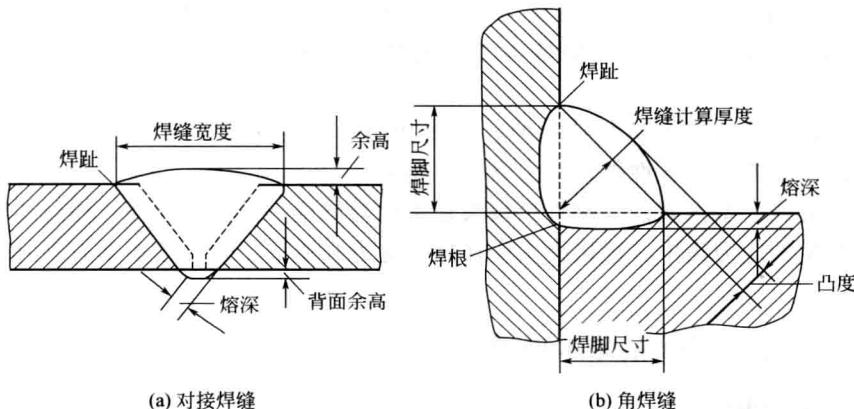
对接焊缝和角焊缝几何形状参数
